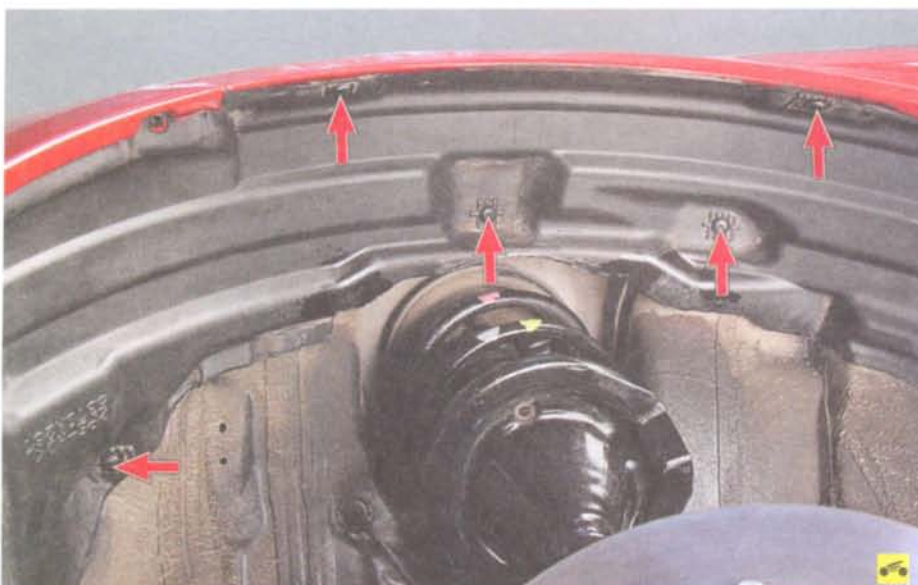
Расположение верхних пистонов крепления подкрылка переднего колеса
